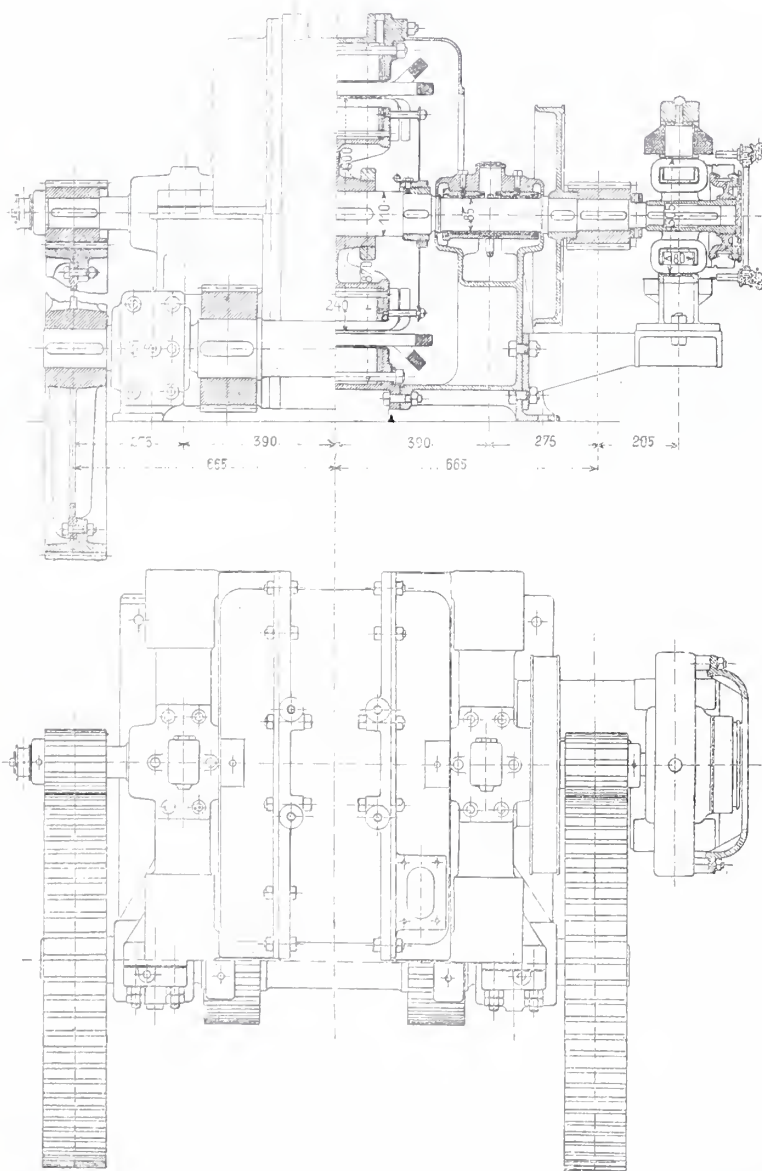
Längsschnitt und Grundriss. 1 : 20.
